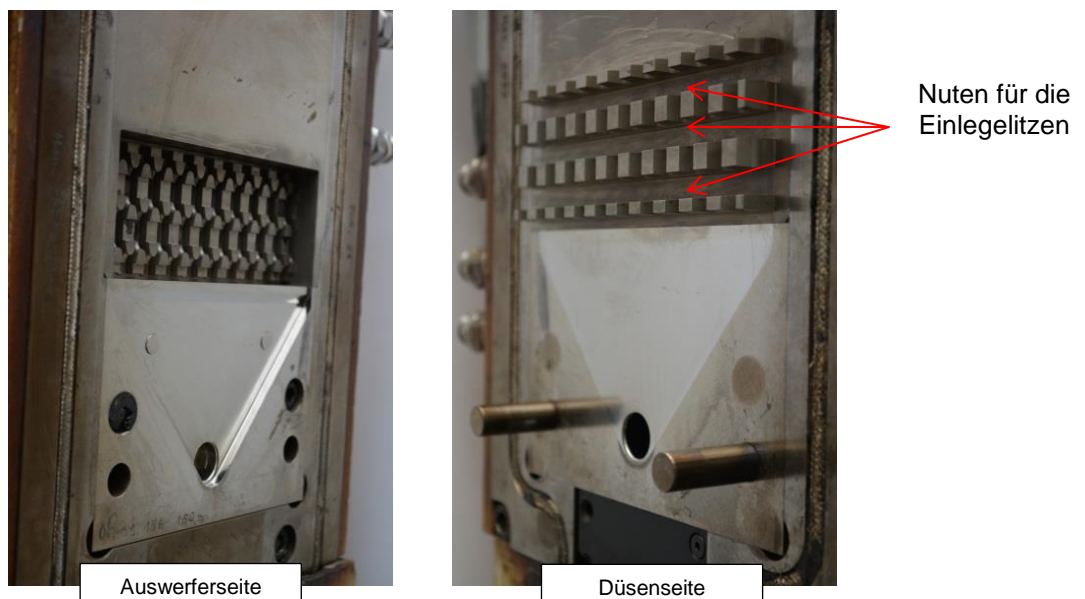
Gefertigte Werkzeugeinsätze mit Zahngeometrie für die Versuchsplatte
